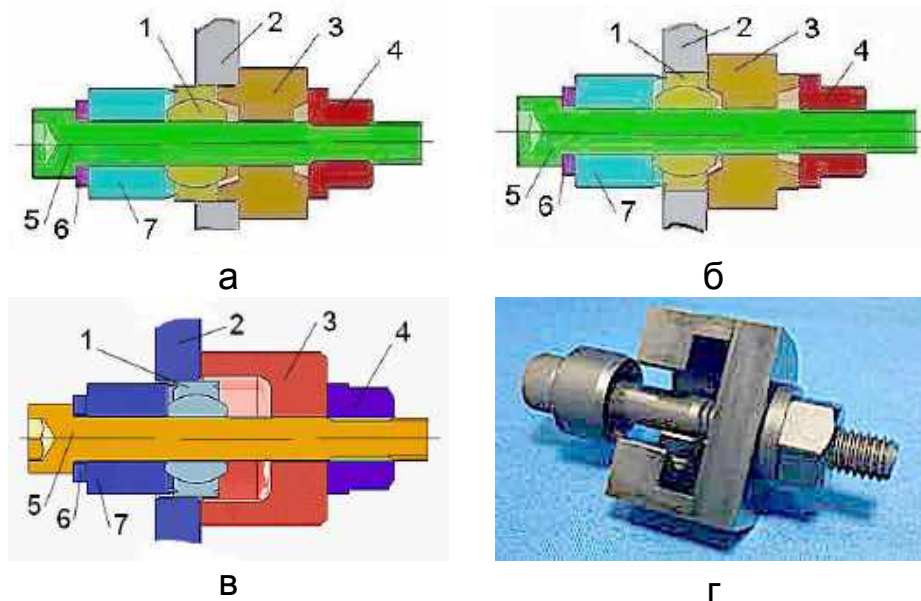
Запресовування та випресовування сферичних підшипників ковзання з конічним V-подібним пазом: 1 – підшипник; 2 – деталь; 3 – опора фасонна; 4 – гайка; 5 – штир; 6 – шайба; 7 – оправка
